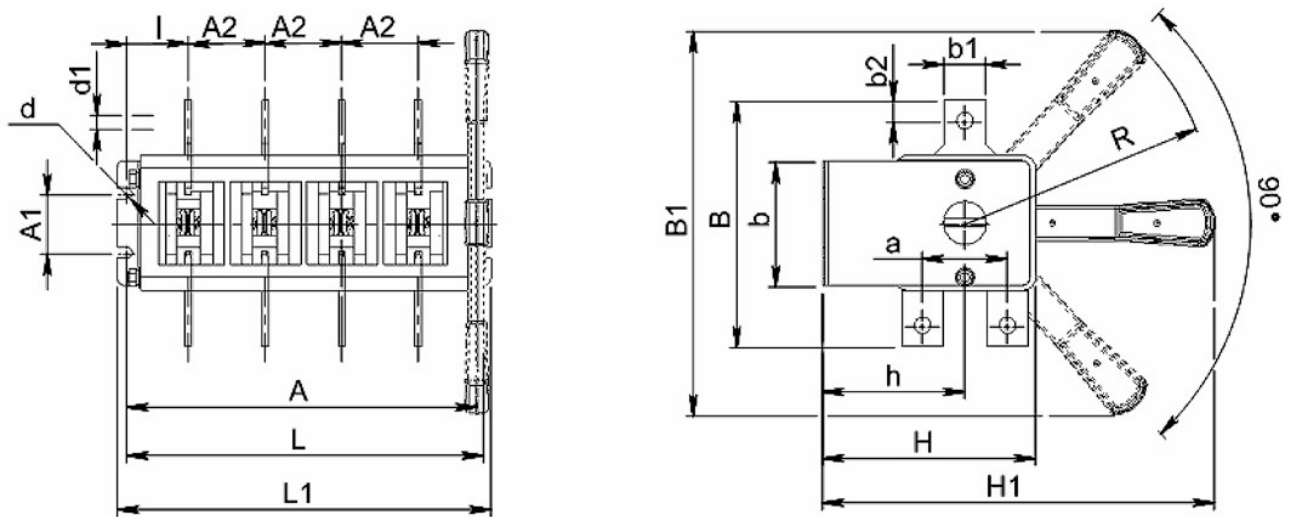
Выключатель-разъединитель на два направления 4-полюсный с боковой рукояткой
